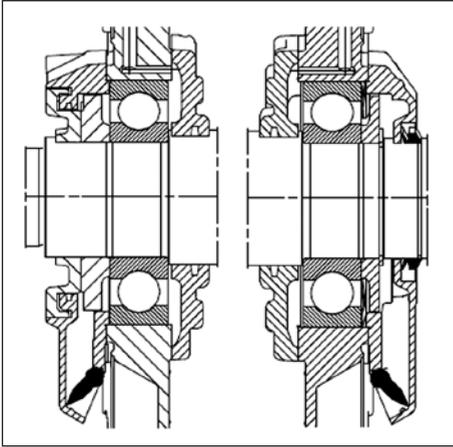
Disposiciones de rodamientos en los motores de hierro fundido para industria de proceso, tamaños 280 a 450
